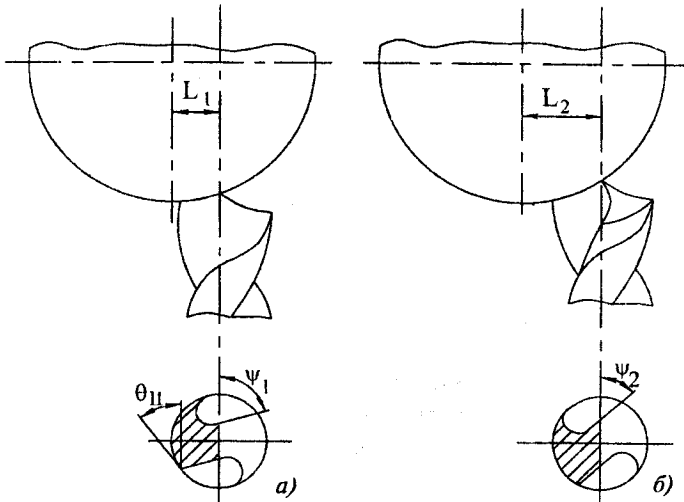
Схема заточування свердла по циліндричній поверхні
